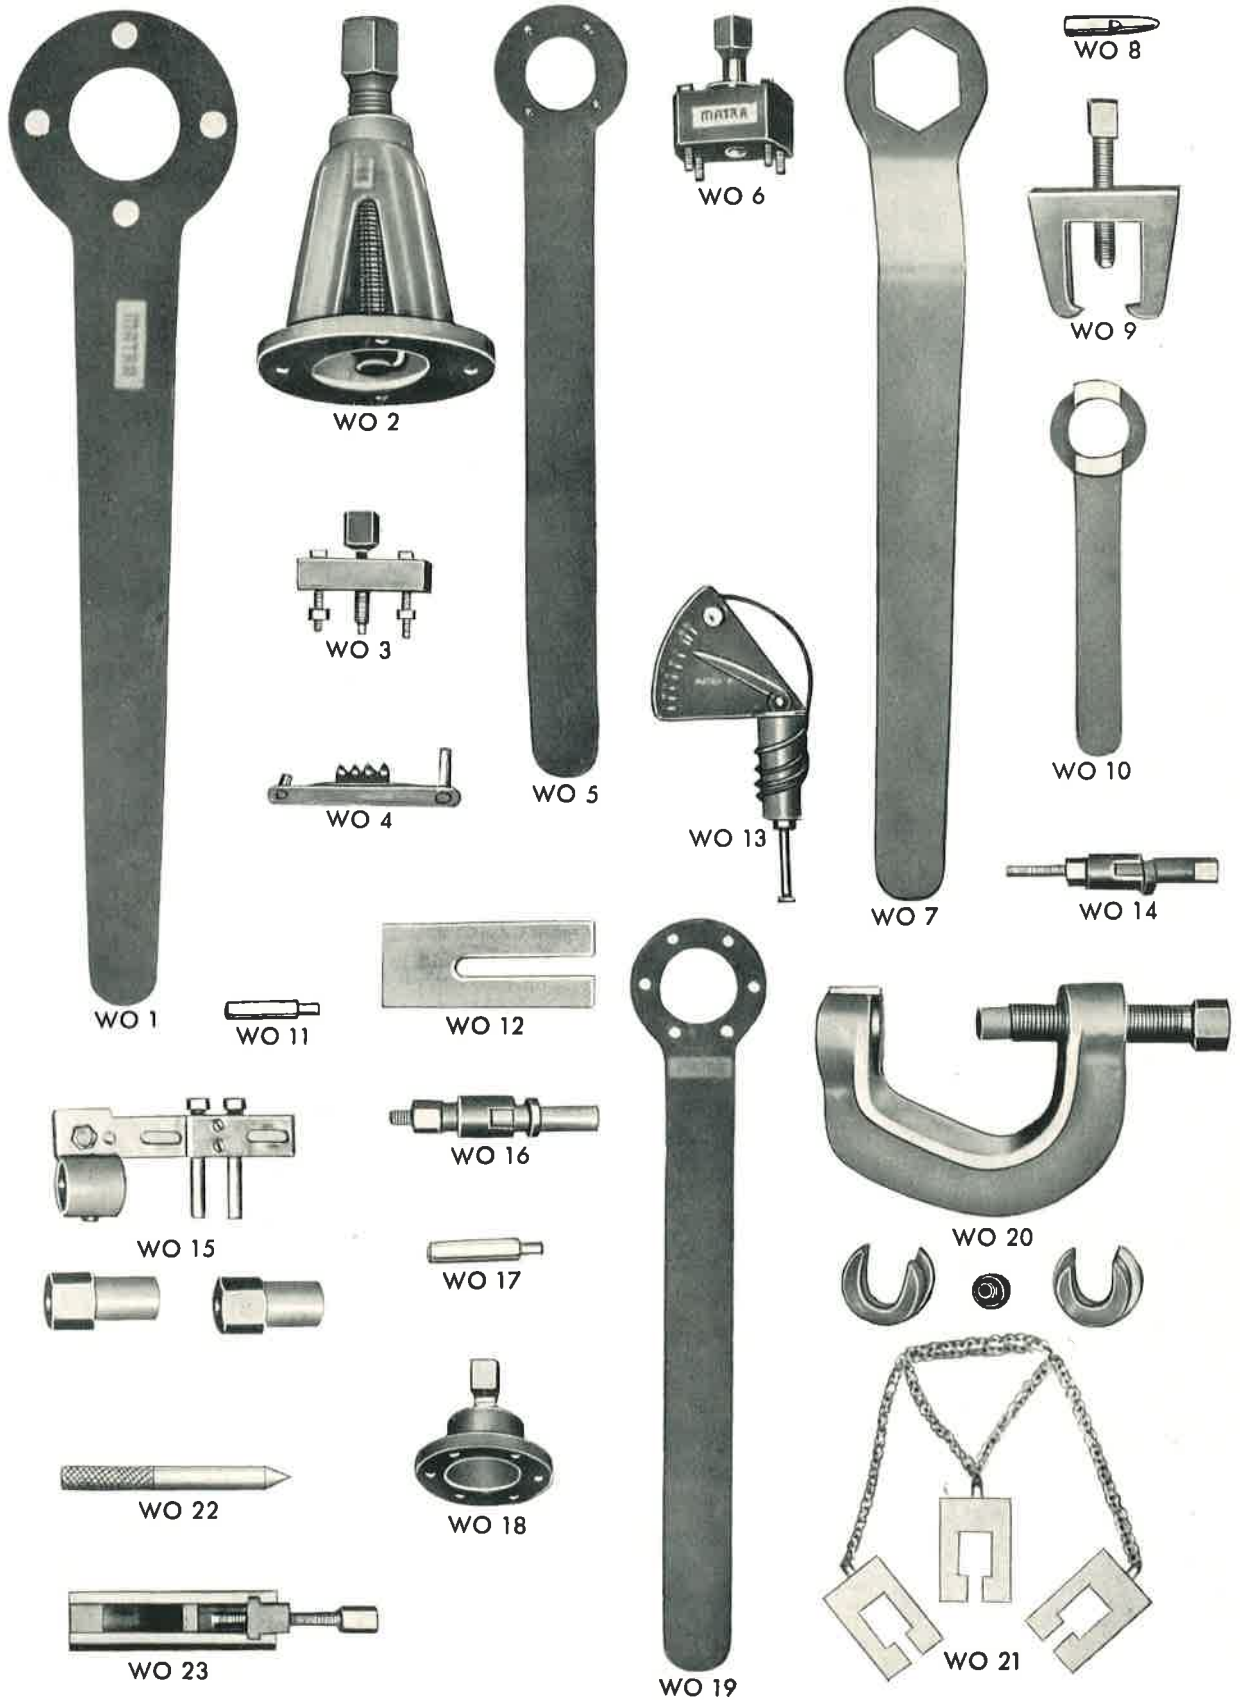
/1: Dieses Bild zeigt alle 23 LLOYD-Spezialwerkzeuge, die z. Z. für fachgerechte Instandsetzungsarbeiten erforderlich sind. Die mit WO bezeichneten Werkzeuge sind gemeinsam mit den Matra-Werken in Frankfurt a. M. entwickelt worden und über die KD-Abteilung des Werkes zu beziehen.
